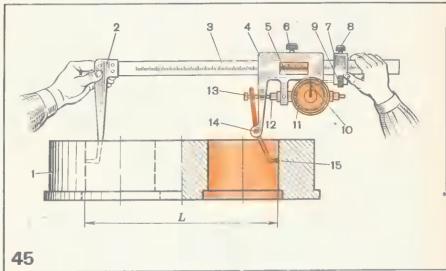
Способ нэмерения профили матрицы штампа штангенциркулем с индикаторным устройством
